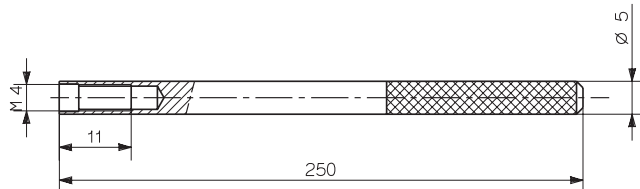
Ausziehwerkzeug für Blindsensor Typ 1319
